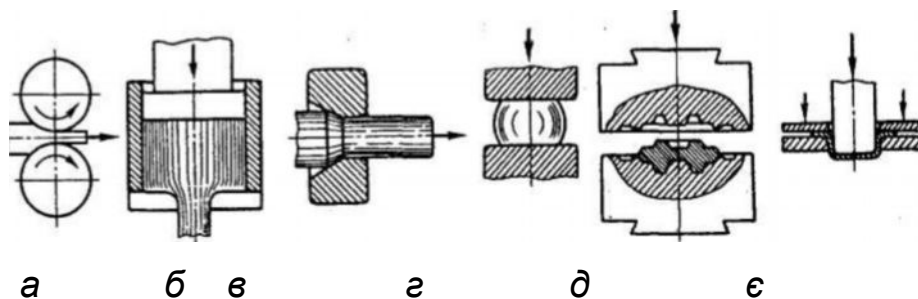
Схеми основних видів обробки металів тиском молотом, пресах або горизонтально-кувальних машинах (рис. 34, д). Форма та розміри внутрішньої порожнини штампа визначають конфігурацію і розміри поковок.
